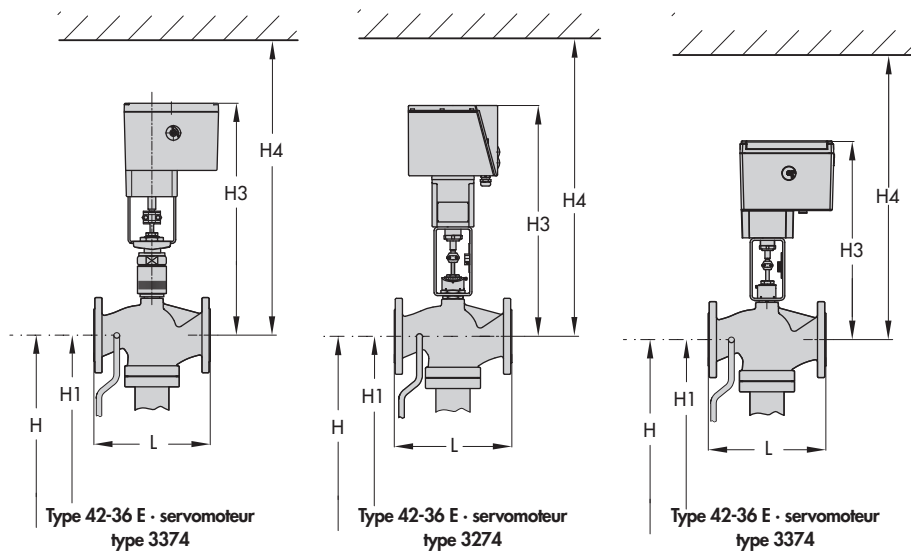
Dimensions des régulateurs, vanne type 2423 E équilibrée par soufflet
